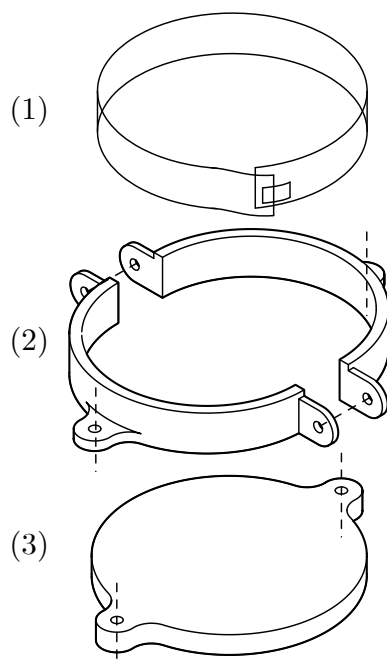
Dessin et assemblage des pièces du moule cylindrique : (1) film rhodoïde cylindrique, (2) faces latérales du moules assemblées par boulonnage (en trait pointillé) (3) Face inférieure du moule assemblée également par boulonnage.
